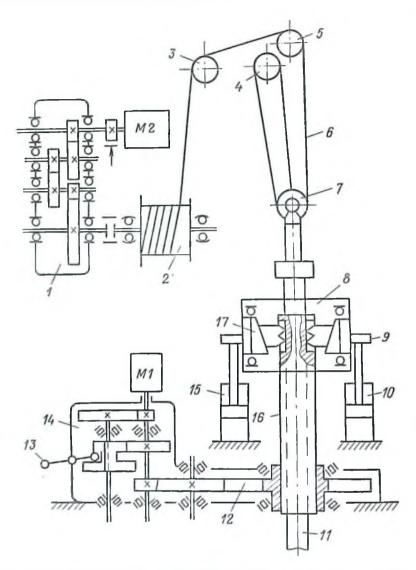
Кинематическая схема вращательно-подающего механизма патронного типа шарошечного станка 2СБШ-200-32
